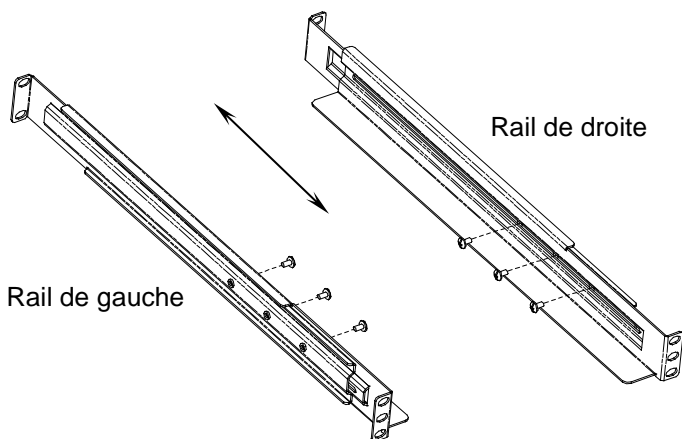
Pré-installation des rails de fixation gauche et droit
